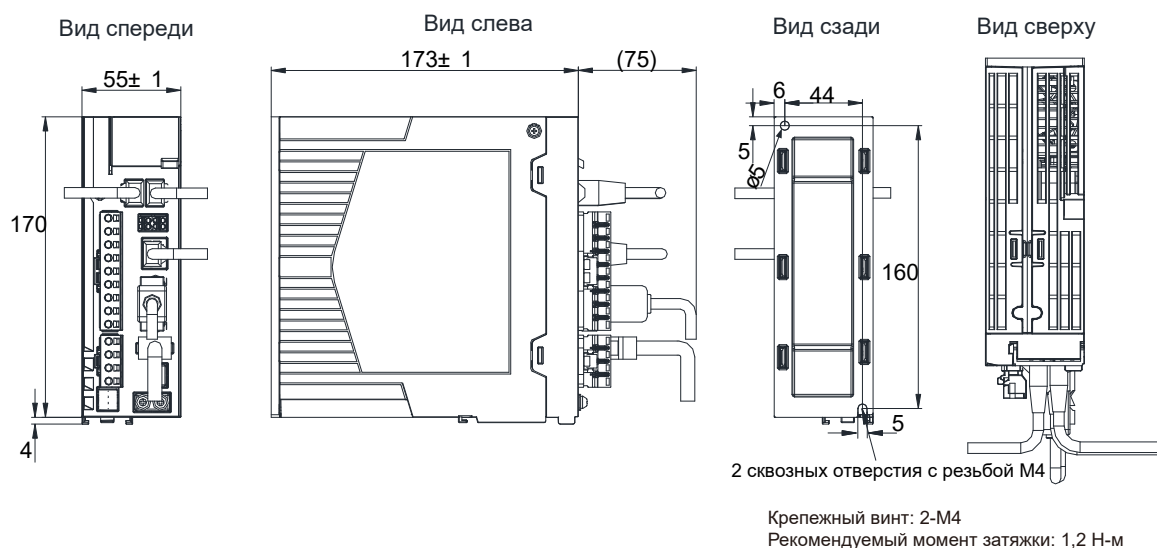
Габаритные размеры для типоразмера С (ед. изм: мм)
